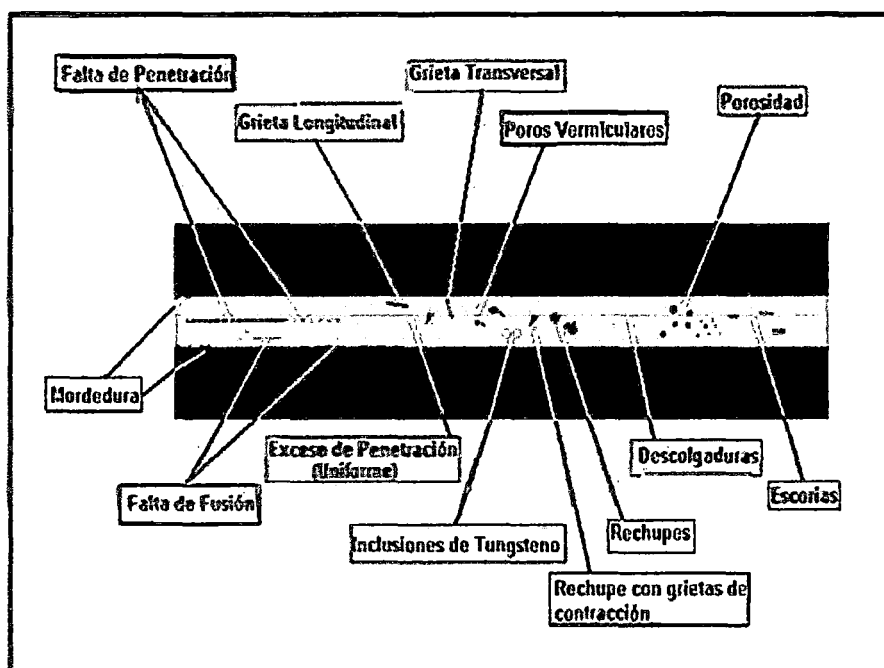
Diversos defectos producidos en la soldadura.
